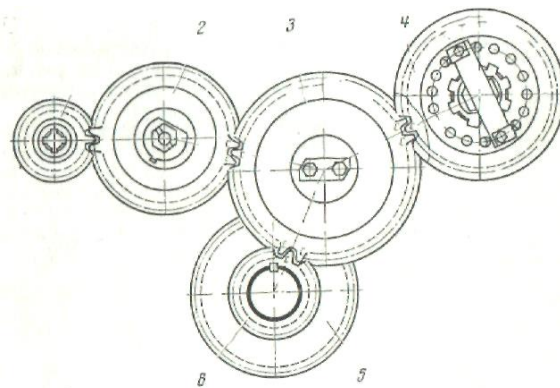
Схема установки шестерень газорозподілу:
